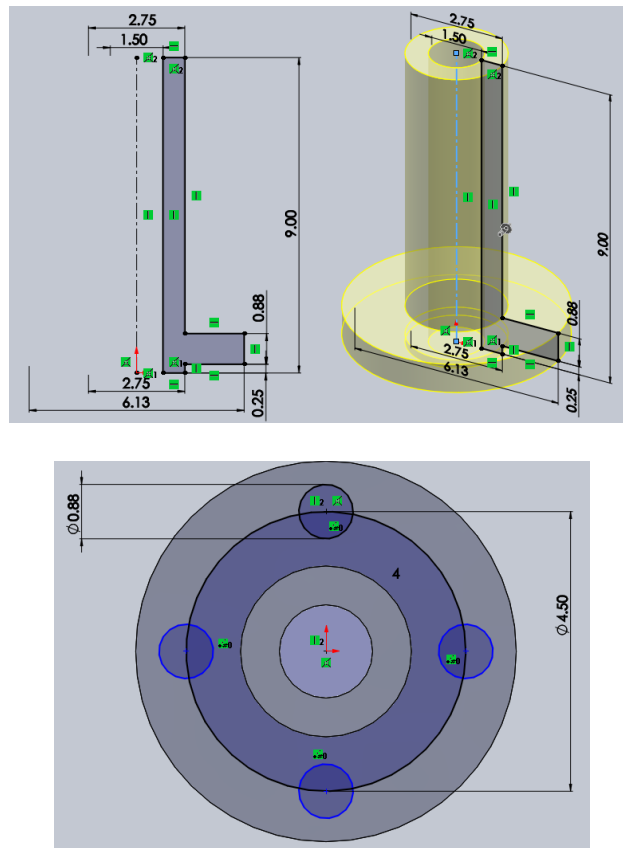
Dimensionamiento de la boquilla en el lado del cabezal. Fuente: SolidWorks
